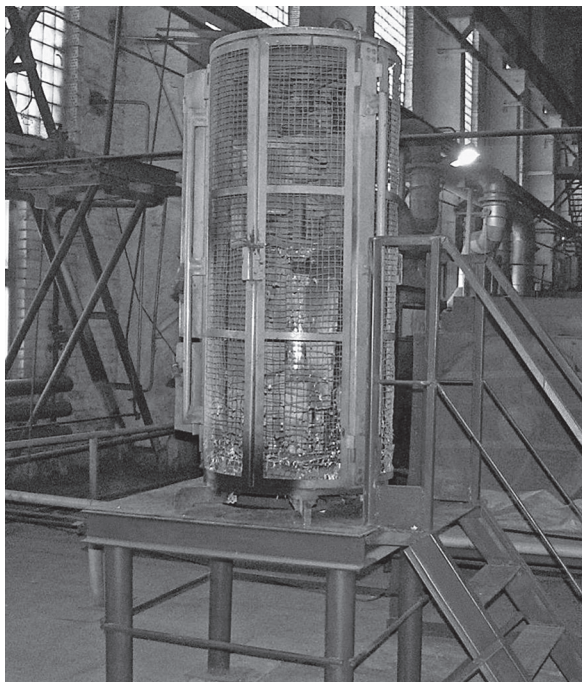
Установка мод. 46161 для металлургической обработки алюминиевого расплава
